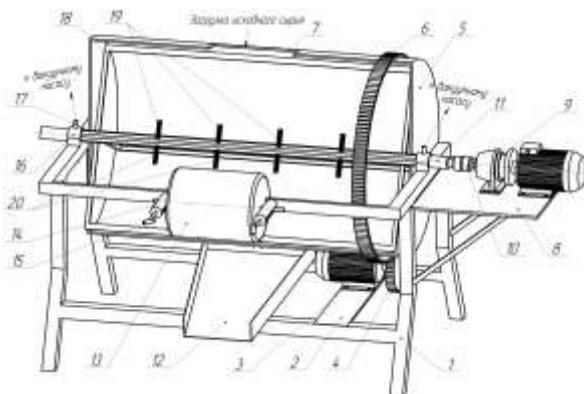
Вакуумный напылитель: 1 – станина; 2 – пластина; 3 – электродвигатель; 4 – зубчатая шестерня; 5 – цилиндрический барабан; 6 – зубчатый венец; 7 – загрузочное отверстие; 8 – площадка; 9 – мотор-редуктор; 10 – муфта; 11 – вал; 12 – лоток; 13 – валик; 14 – подпружиненные регулирующие устройства; 15 – рукоятка; 16 – подшипниковые опоры; 17 – патрубок; 18 – рамная мешалка; 19 – насадки; 20 – распылительные форсунки
